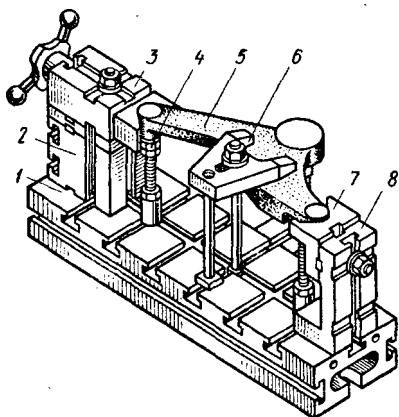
Универсально-сборное приспособление для фрезерования бобышек у рычагов
